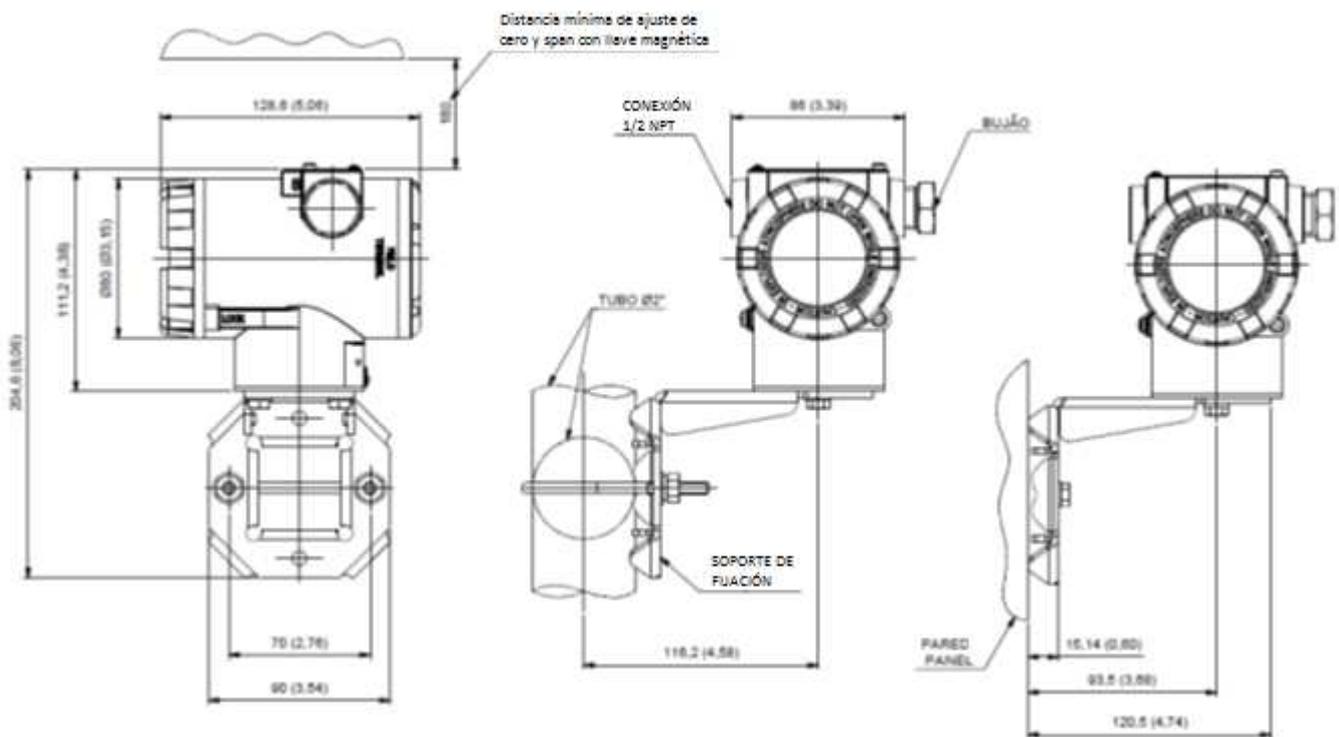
Diseño dimensional y esquema de montaje del VRI10-I.
